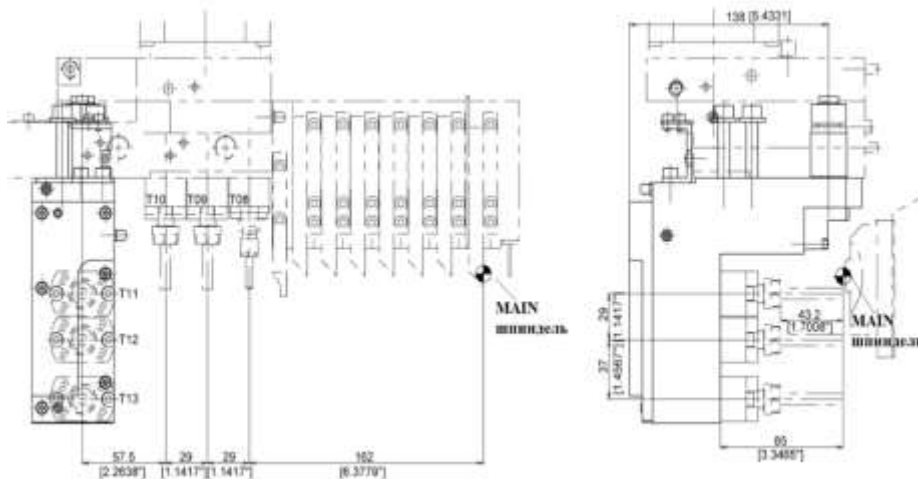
Кінематична схема компанування верстата Cincom L12 2M10
